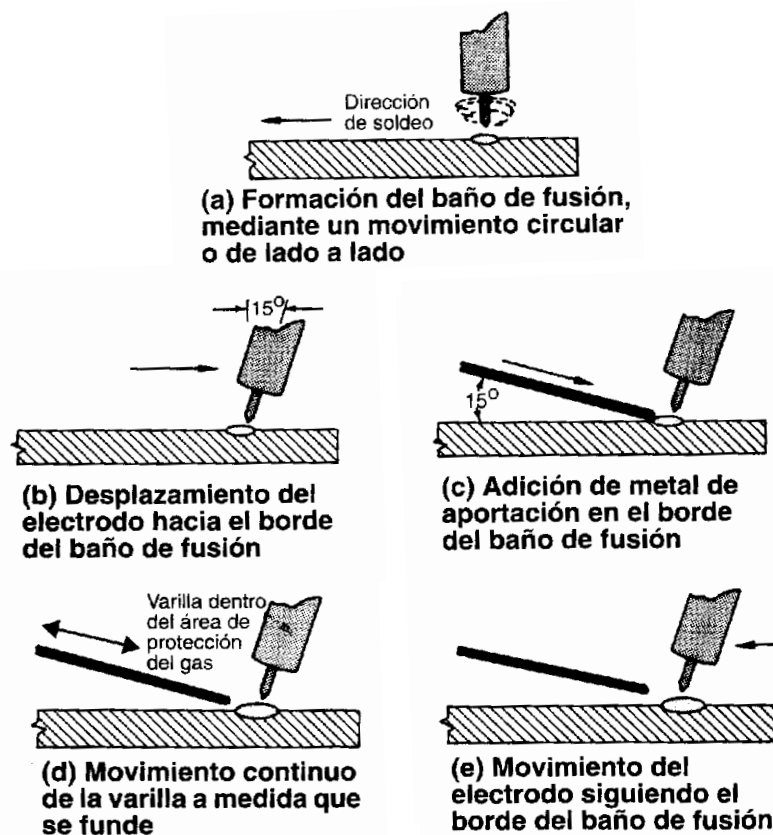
Pasos para producir una soldadura TIG
